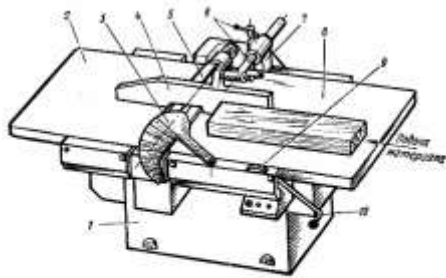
Одношпиндельный фуговальный станок СФ6-1:
